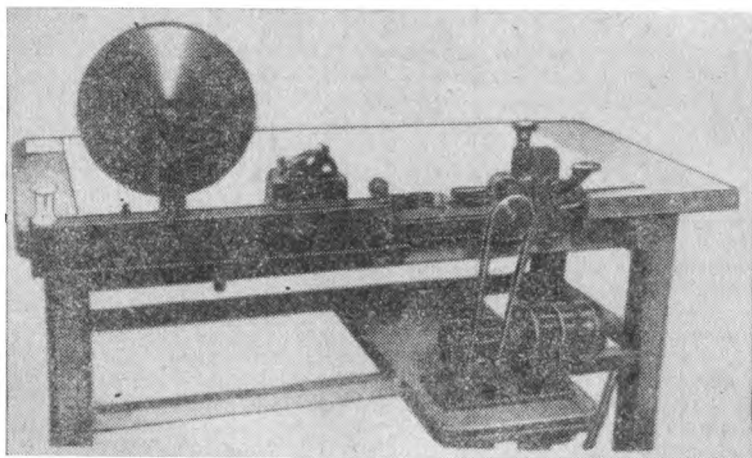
Машина для окантовки чертежей ОКМ.
